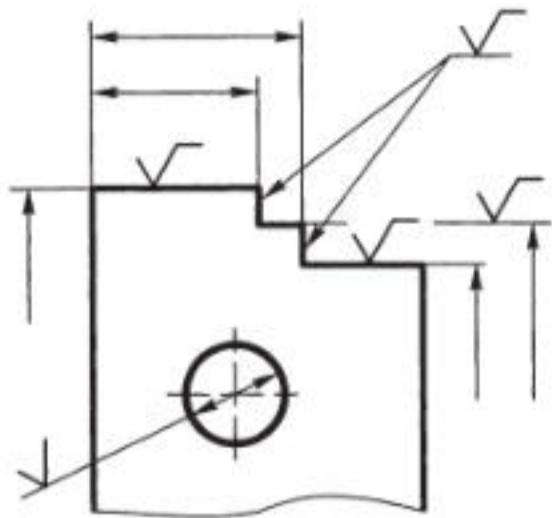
Пример расположения обозначений шероховатости поверхности
